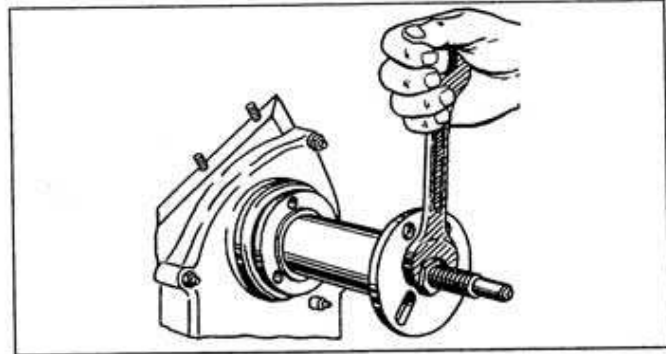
Напрессовка ступицы шкива коленчатого вала с помощью приспособления 16-У-236817
